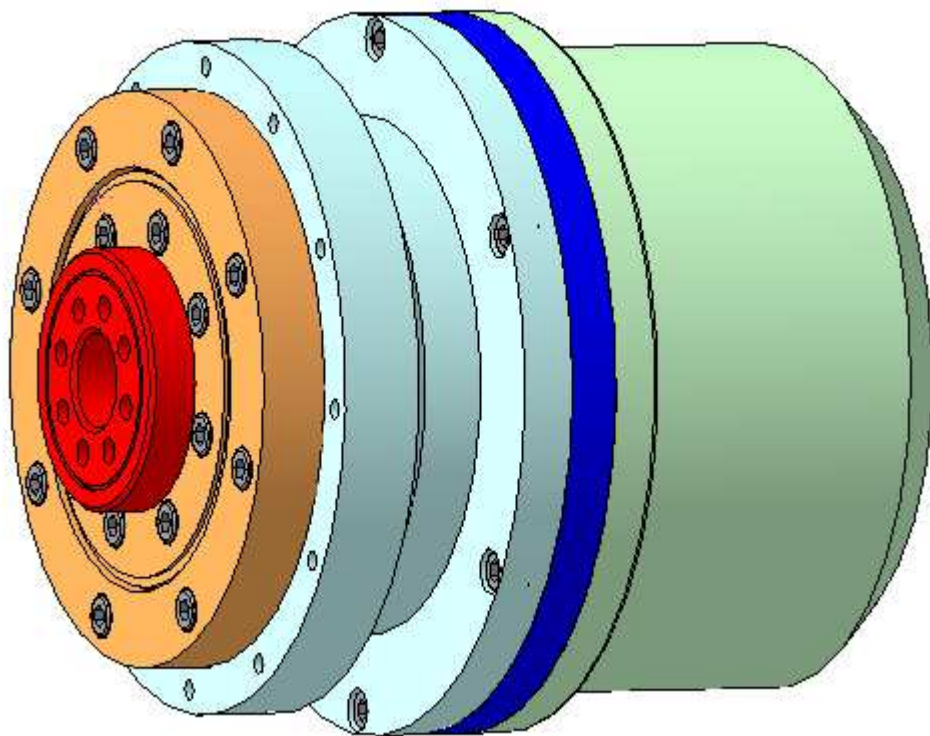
Установленный подшипник со скрепляющимися роликами
